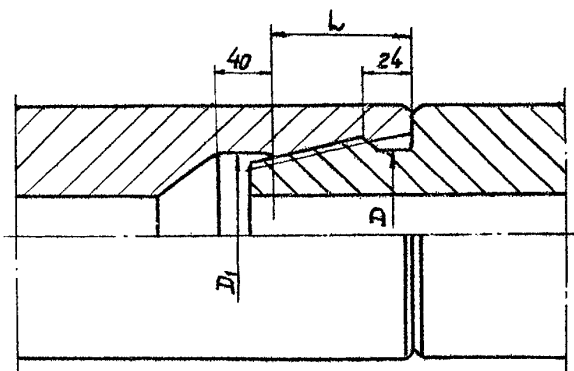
Резьбовое соединение с наружным упорным торцом с резьбовыми разгружающими канавками.
